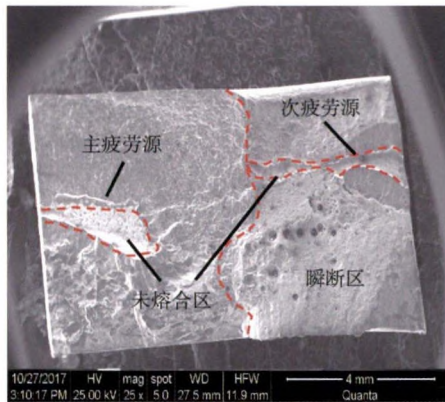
5A06-O/7A05-T6 对接接头疲劳断口(气孔缺陷)
